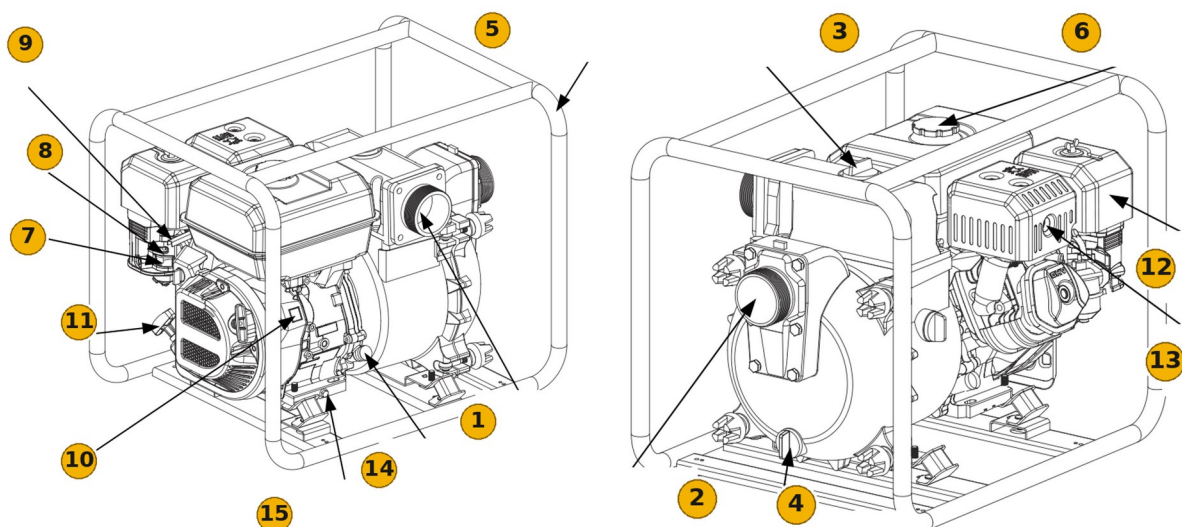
Motobombas TRASH: vista do lado do motor e do lado da bomba
